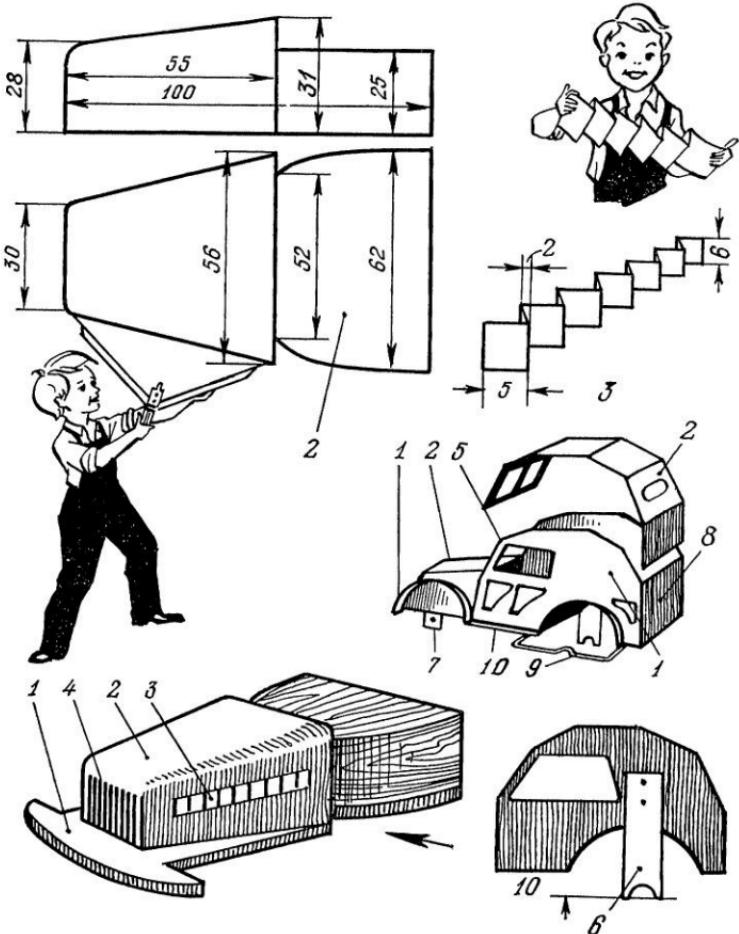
Капот мотора и сборка деталей кузова вездехода:
